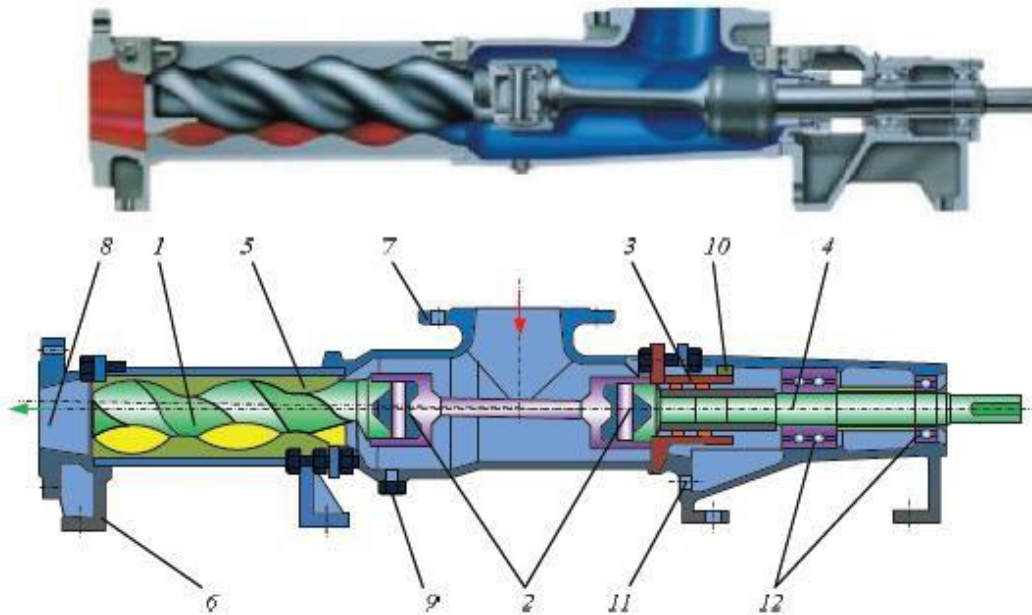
Pompă cu un șurub. 1- rotor elicoidal; 2- articulații cardanice sau sferice; 3- garnituri inelare; 4- arbore; 5- stator ; 6- postament; 7- flanșă de aspirație; 8- flanșă de refulare; 9- orificiu pentru manometru; 10- presetupa ; 11- orificiu pentru drenare; 12- lagăr de rostogolire.
